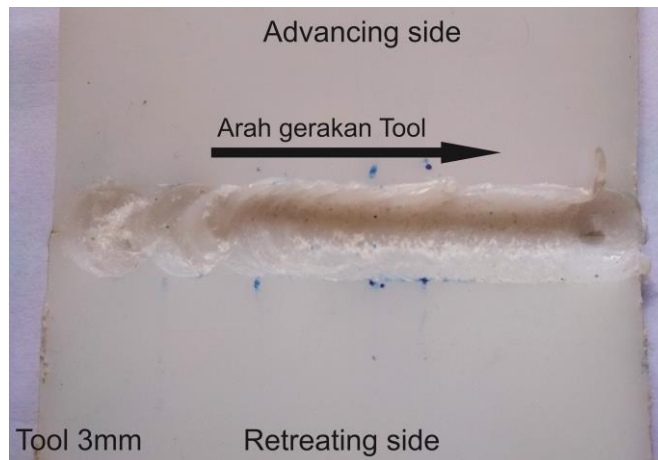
Hasil pengelasan pin silinder ulir 3mm
